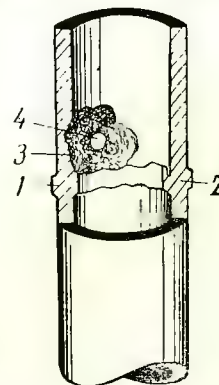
Вид в разрезе экранной трубы котла ТП-170-1, рассчитанного на давление 100 ат, с коррозией над контактным сварным стыком.
